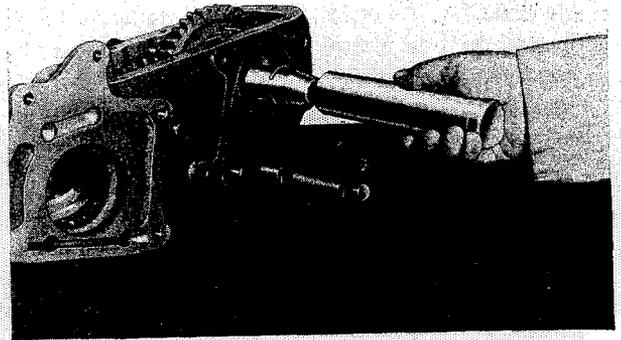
Einbauwerkzeug für Sicherungsring der Ausgangswelle
